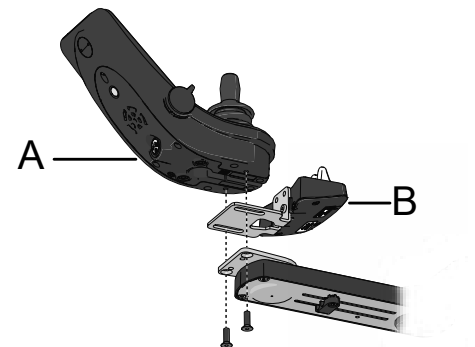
Das Steuerpult ist mit zwei Schrauben auf dem Parallelpulthalter befestigt.
